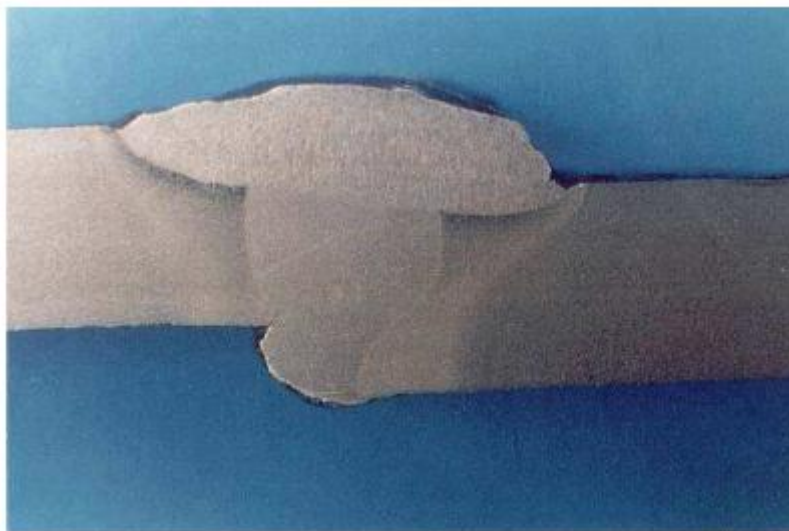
Caniveaux en surface de joint soudé.
